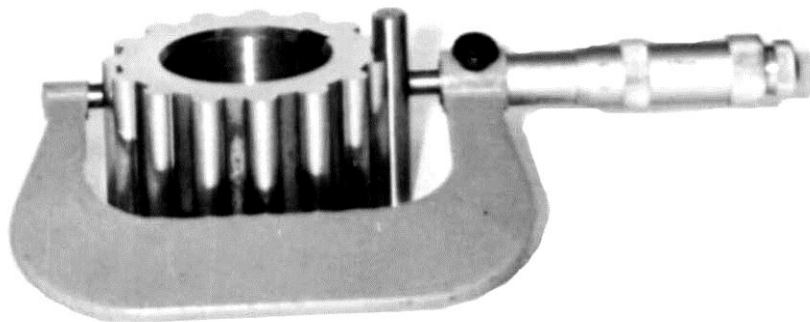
Измерение погрешности формы зубчатого контура шестерни (параметр $1б$)
